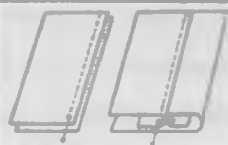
Обтачной шов со сложной рамкой с закреплением шва с лицевой стороны
